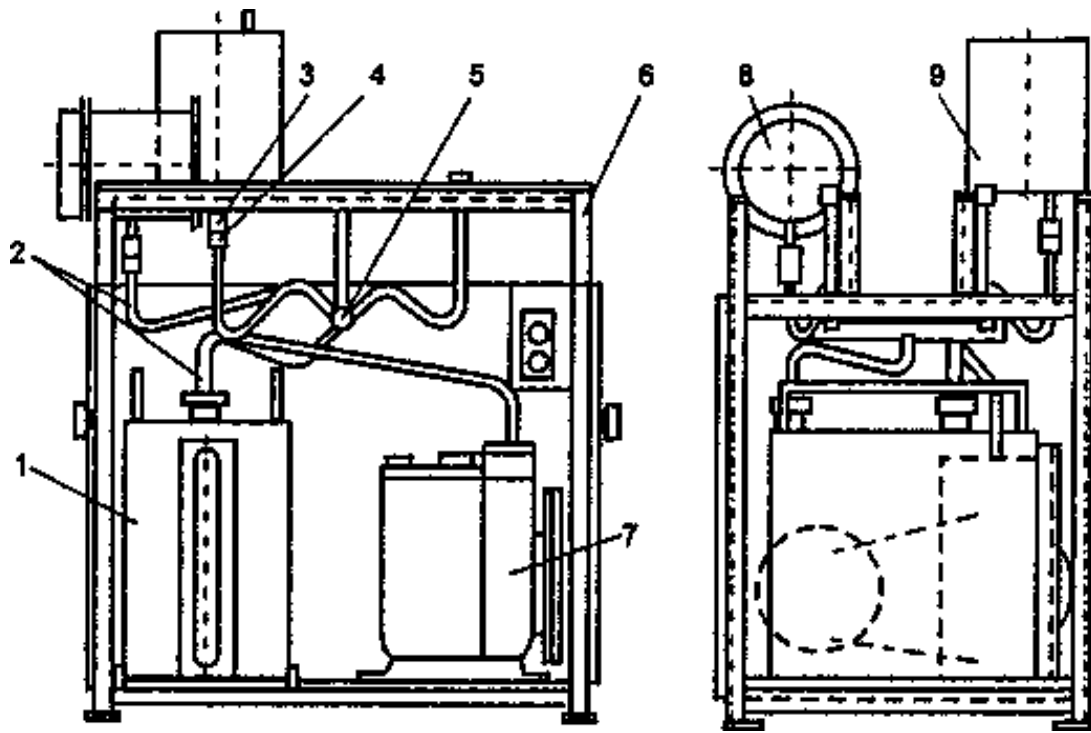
Установка для прискороного зливу масла з мотор-компресорів холодильників: 1 - бак для зливу масла; 2 - вакуумні шланги; 3 - напівмуфта затискна ИП-24; 4 - напівмуфта швидкознімна ИП-24; 5 - колектор; 6 - корпус установки; 7 - вакуумний агрегат ВН-461М; 8, 9 - мотор-компресор горизонтального і вертикального виконання
